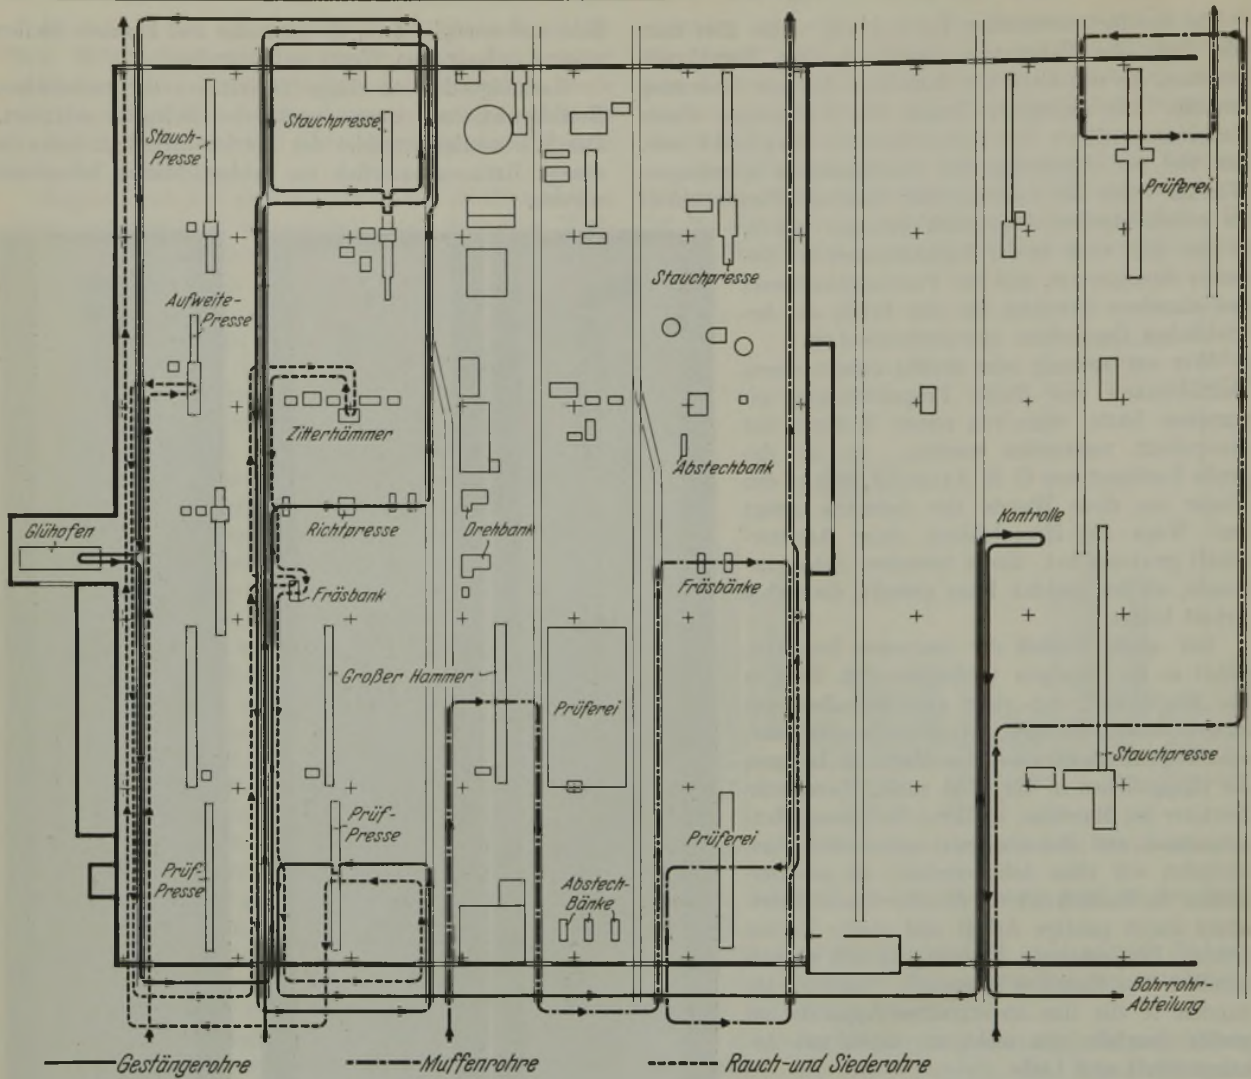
Lageplan mit Förderwegen einzelner Rohrarten vor dem Umbau.
